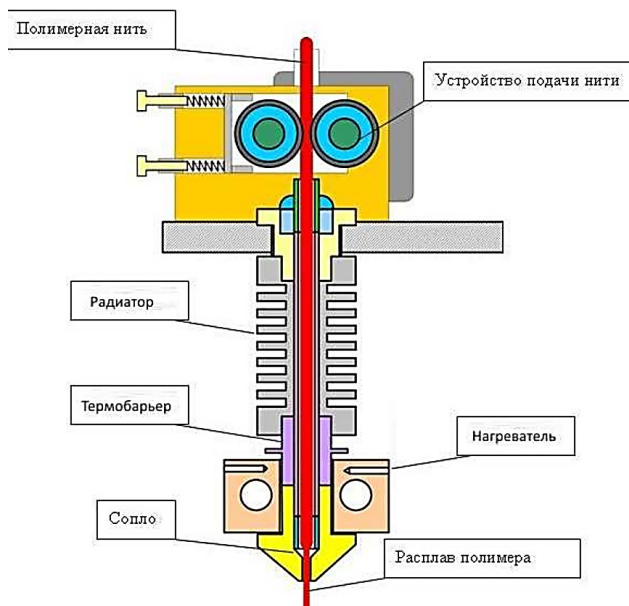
Компоновочная схема экструдера печатающей головки
